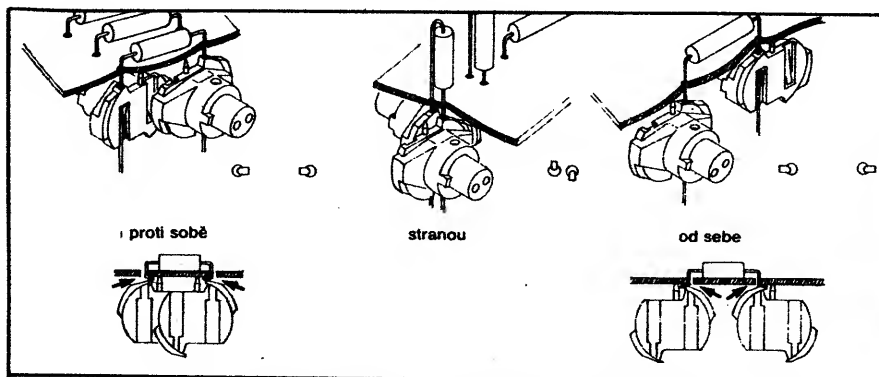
Princip mechanismu pro stříhání a ohýbání vývodů jedním nástrojem
